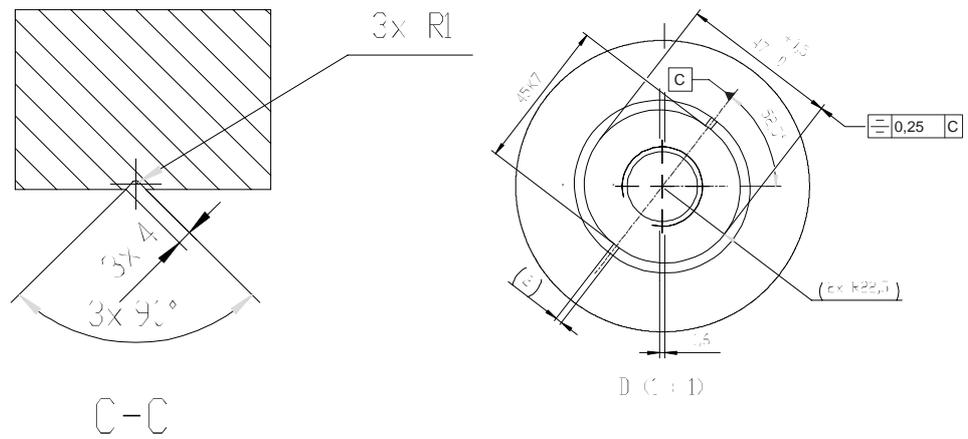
Sections de la plaque d'assise (dimensions en mm).
